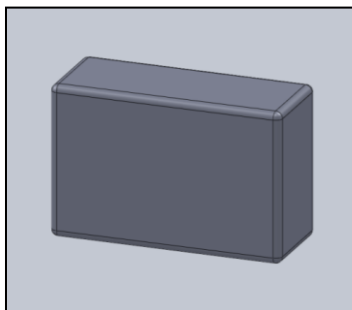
Cubo para fabricar un molde utilizando SolidWorks®.
